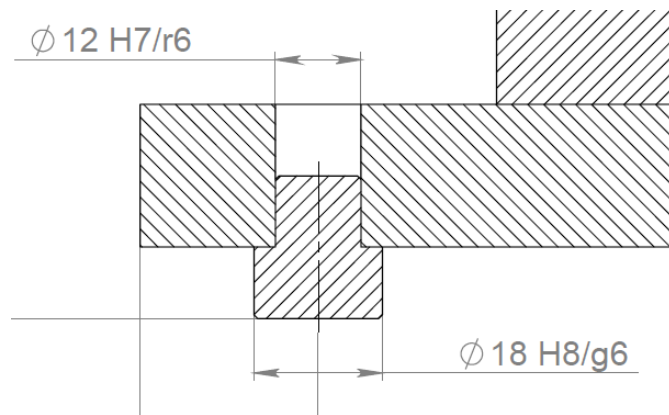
Посадки установчого пальця в корпуса на в Т-подібні пази стола верстату
